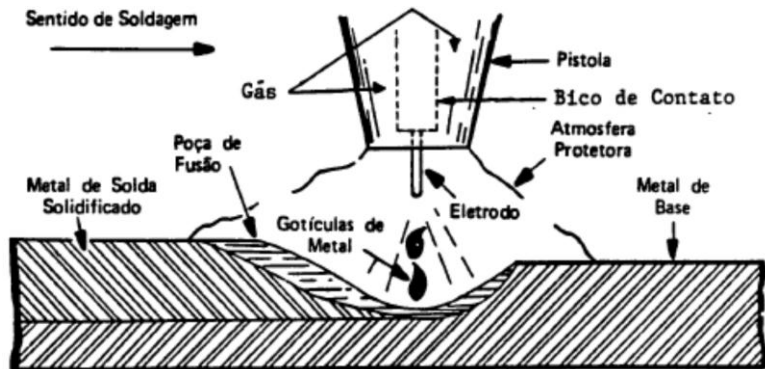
Soldagem a arco elétrico com arame tubular com proteção gasosa (AWS, 1998).
